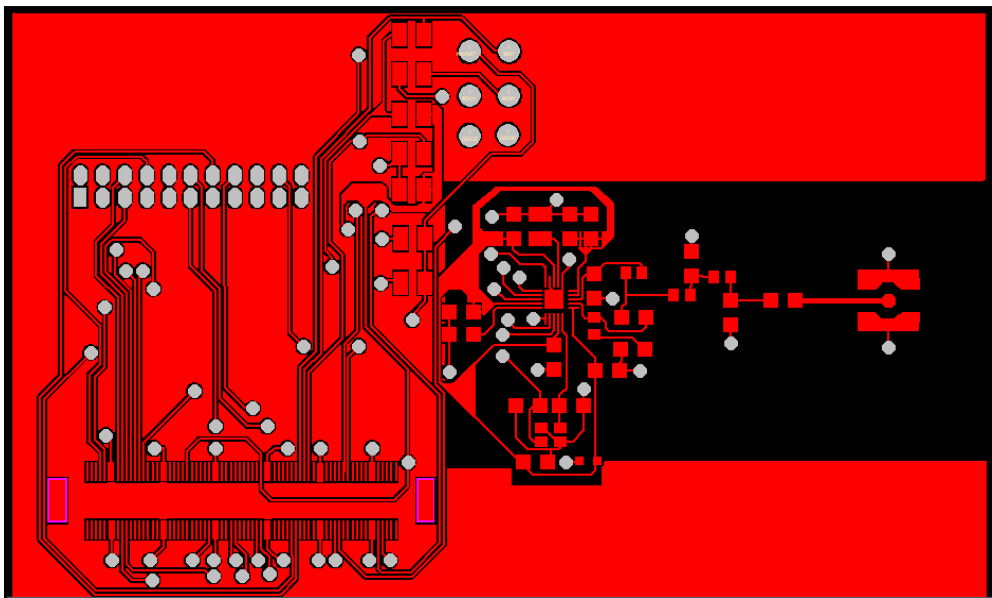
PCB fresado para el montaje de la etapa de radio (Top Layer).
